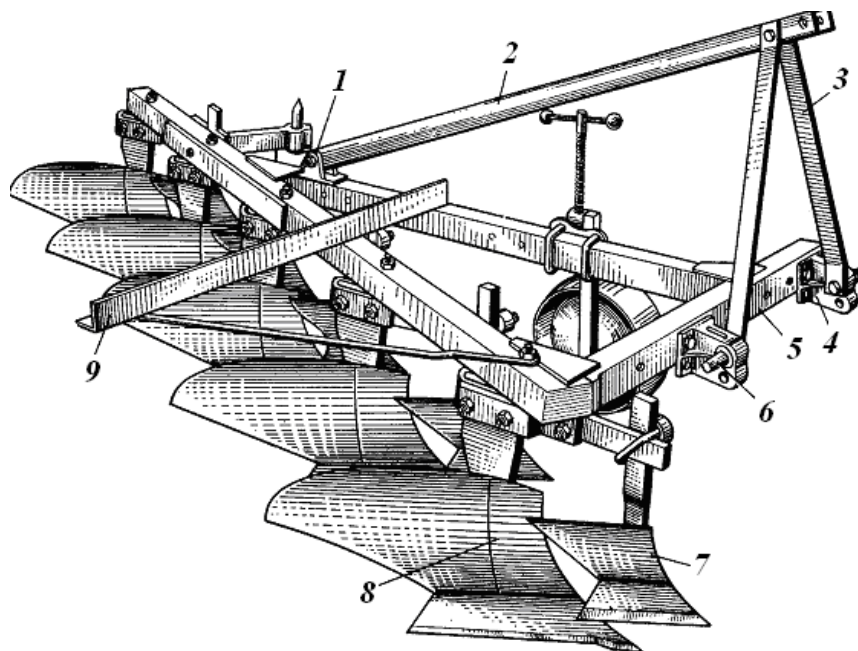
Плуг начіпний п'ятикорпусний ПЛН-5-35: 1, 4 - кронштейни; 2 - розкіс; 3 - стояк; 5 - рама; 6 - палець; 7 - передплужник; 8 - корпус; 9 - причіп для борін
